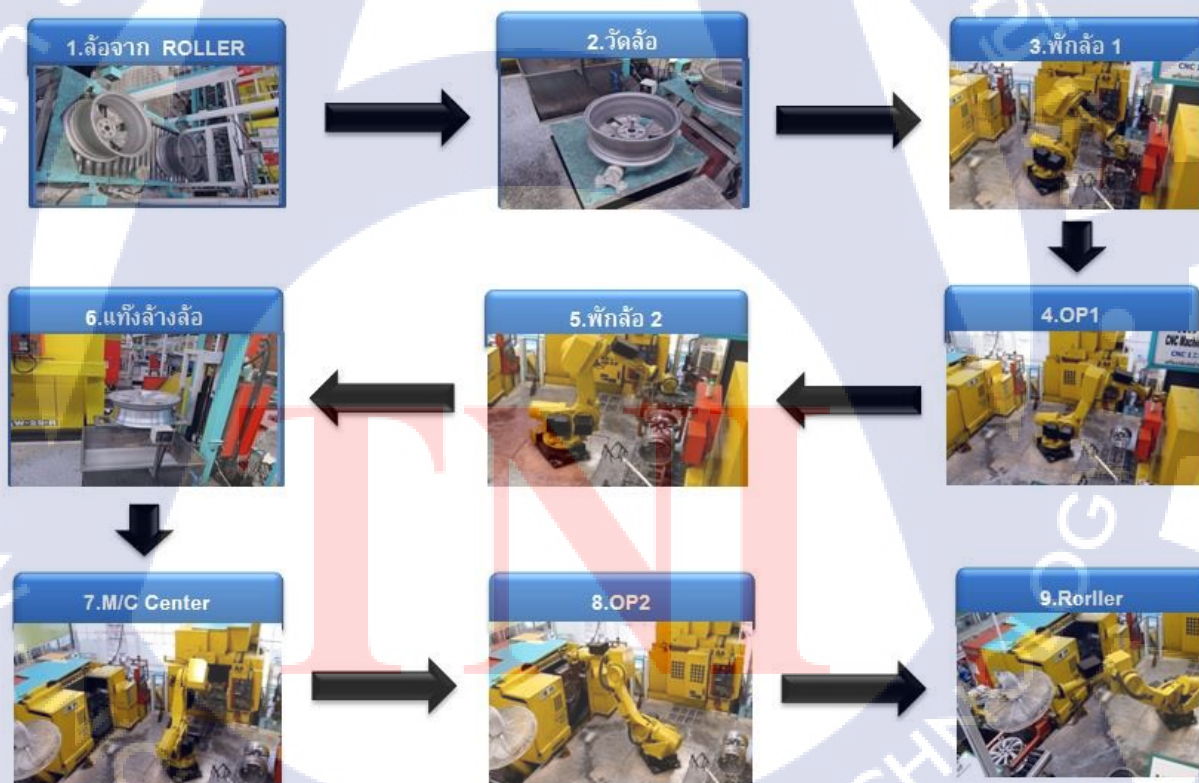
CNC Machine Center (เครื่องเจาะรู PCD)
